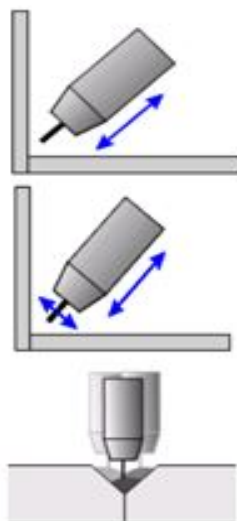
Система отслеживания сварного шва «COMARC»
